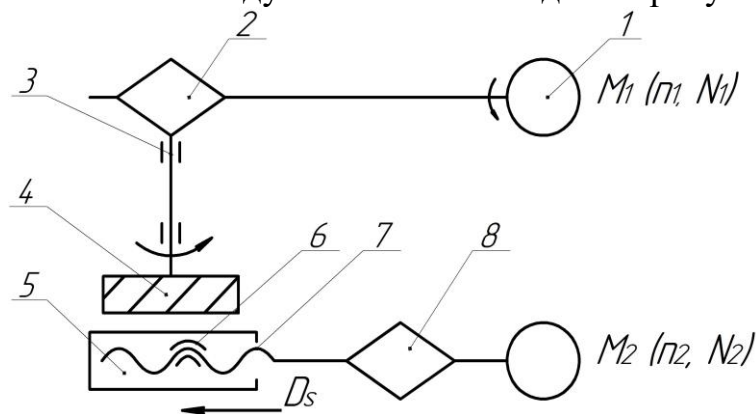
Структурно-кінематична схема консольного вертикально-фрезерного верстата: 1 – електродвигун головного руху; 2 – коробка швидкостей; 3 – шпиндель; 4 – фреза; 5 – стіл; 6 – гайка; 7 – гвинт; 8 – коробка подач; 9 – електродвигун допоміжного руху D_s .
